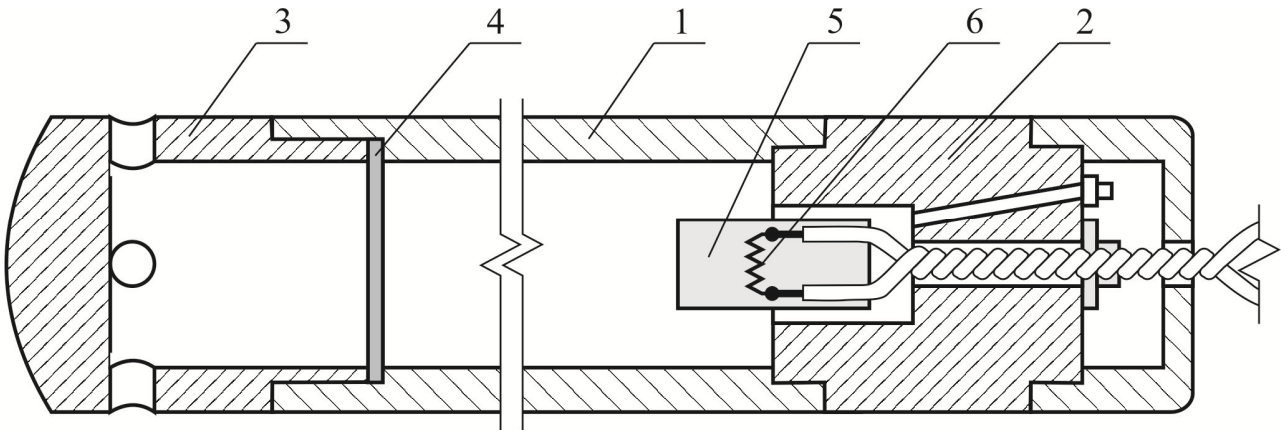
Конструкція патрона кардокс: 1 – порожній сталевий циліндр; 2 – зарядна голівка; 3 – розрядна голівка; 4 – сталевий диск; 5 – нагрівальний патрон; 6 – електрозапалювач
